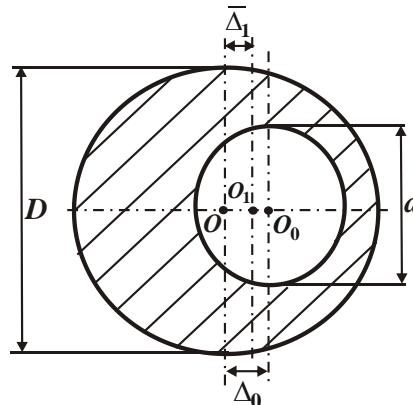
Розрахункова схема визначення величини упругого переміщення сверла при расверливанні отверстия з початковим діаметром d
